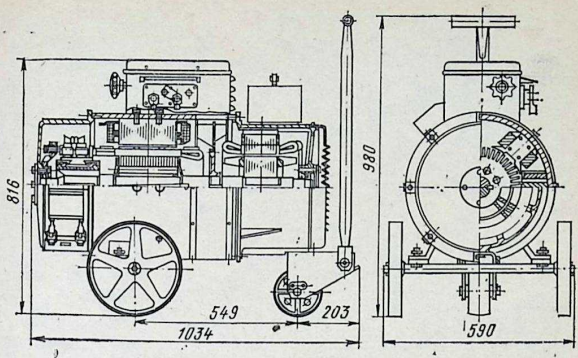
Сварочный преобразователь ПСО-300.
